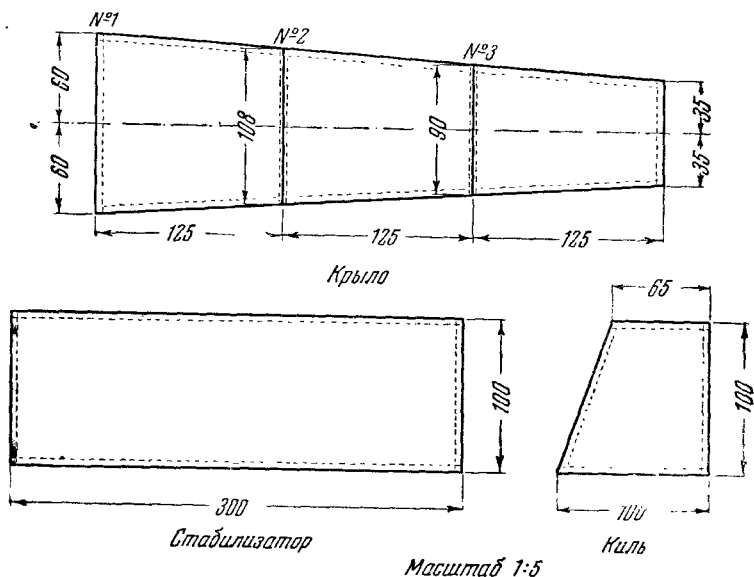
Рабочие чертежи крыла, стабилизатора и киля
